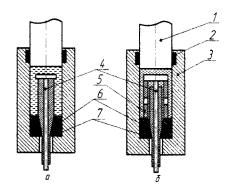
Схемы гидропрессования труб на подвижной (а) и неподвижной (б) оправках: 1 – плунжер; 2- уплотнение; 3 – контейнер; 4 – оправка; 5 – опора; 6 - уплотнение; 7 - матрица
